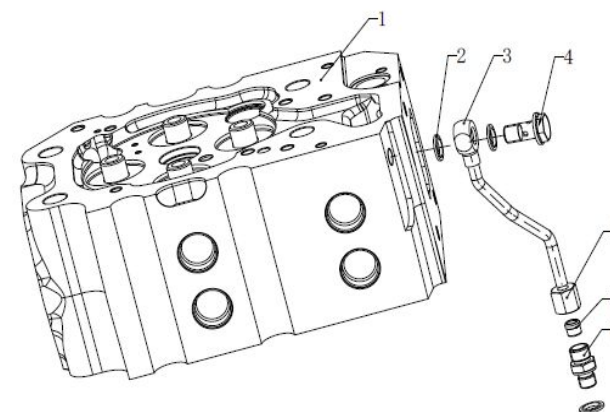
Сборочный чертеж маслопровода коромысла 16M33
